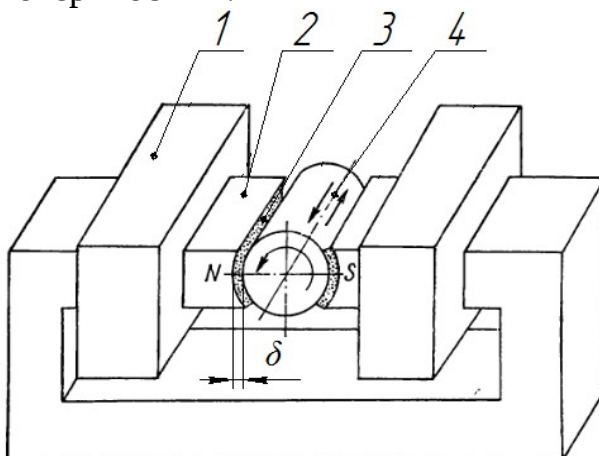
Схема МАО наружных цилиндрических поверхностей: 1 – электромагнитная система; 2 – полюсные наконечники; 3 – ФАП; 4 – обрабатываемая деталь
